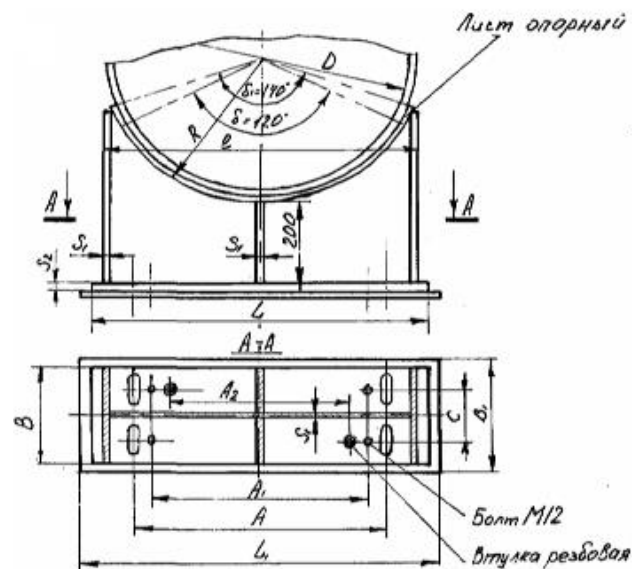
Конструкция стандартных седловых опор под стальные сварные горизонтальные цилиндрические аппараты
